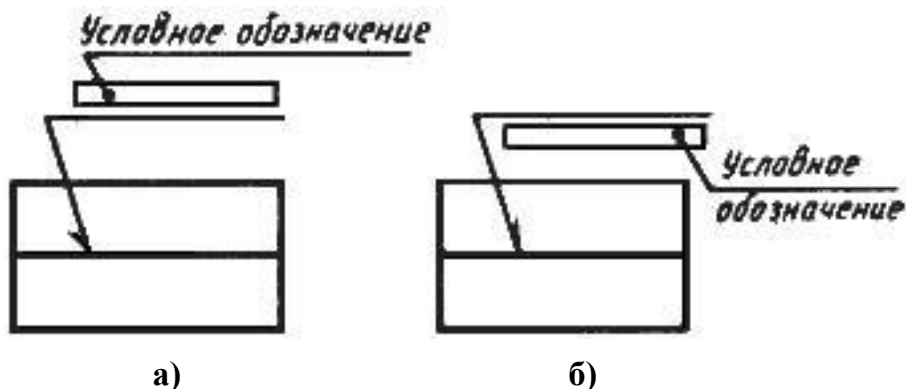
Обозначение нестандартного шва [5]: а – с лицевой стороны; б – с оборотной стороны
